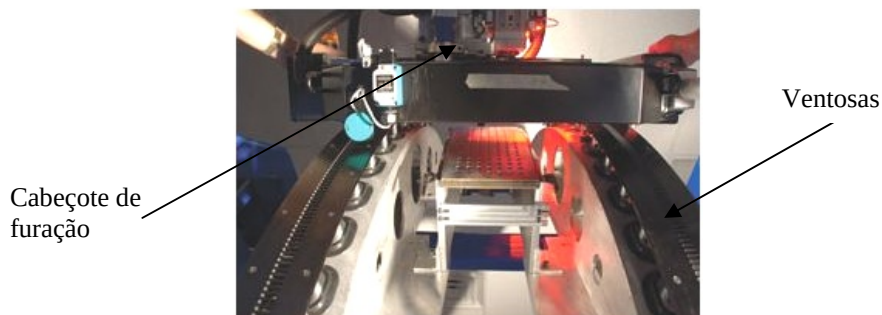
Sistema *Flex Track* utilizado para furação de grandes segmentos estruturais. [3]
